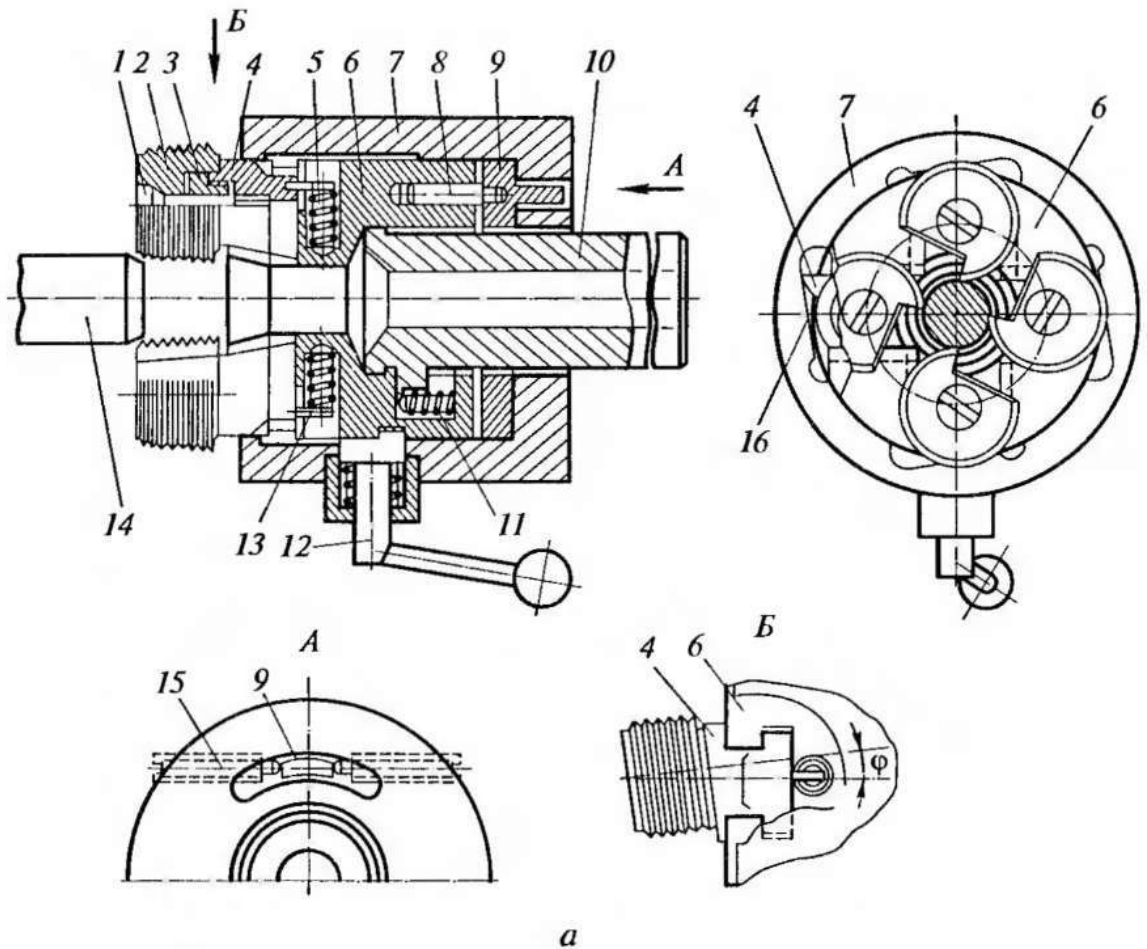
Гвинторізна головка, що не обертається в робочому положенні
